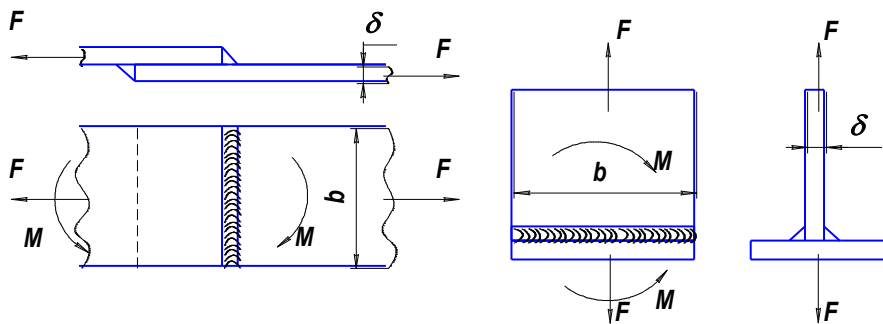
Схемы нагружения сварных соединений:
